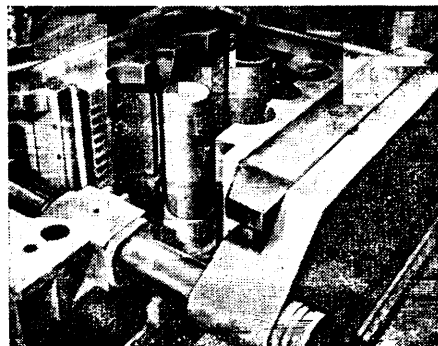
Облицованный кокиль для литья гильз цилиндров
